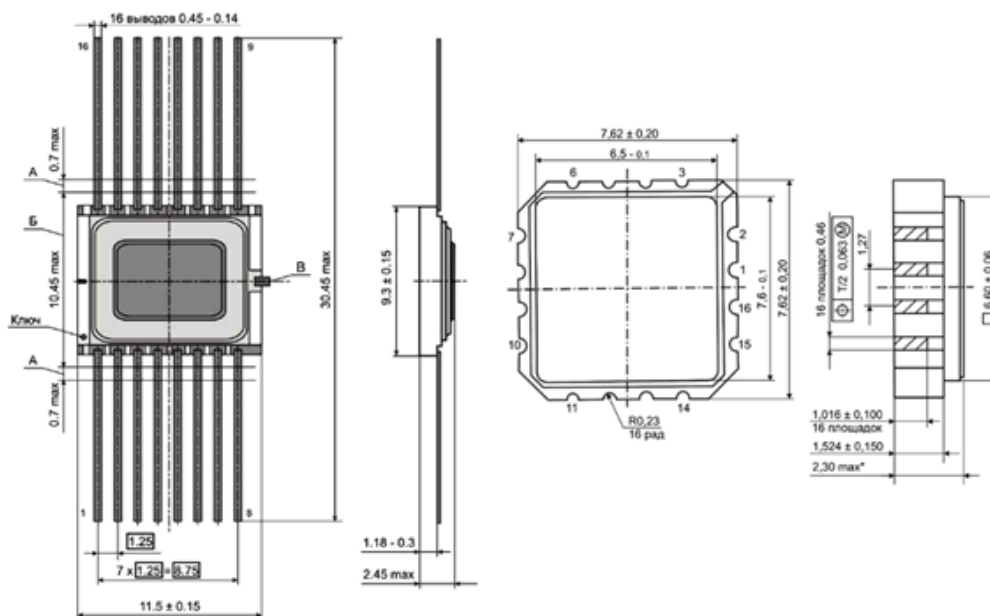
размеры корпусов микросхем 1363EU1U
